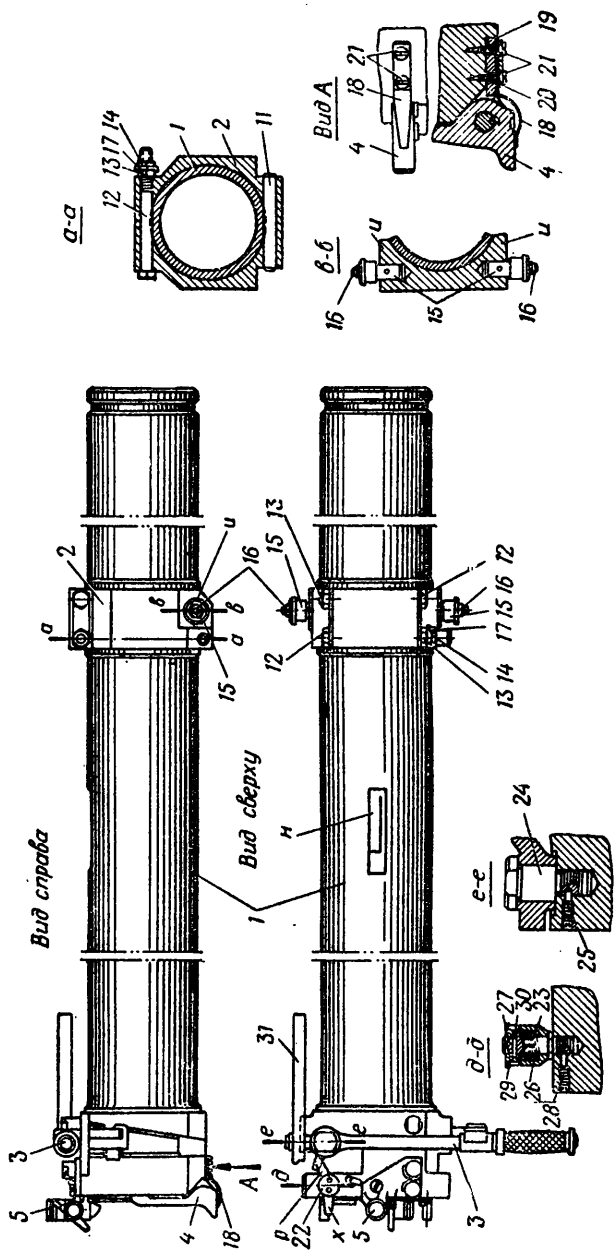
Качающаяся часть миномета новой конструкции (общий вид и сечения):
